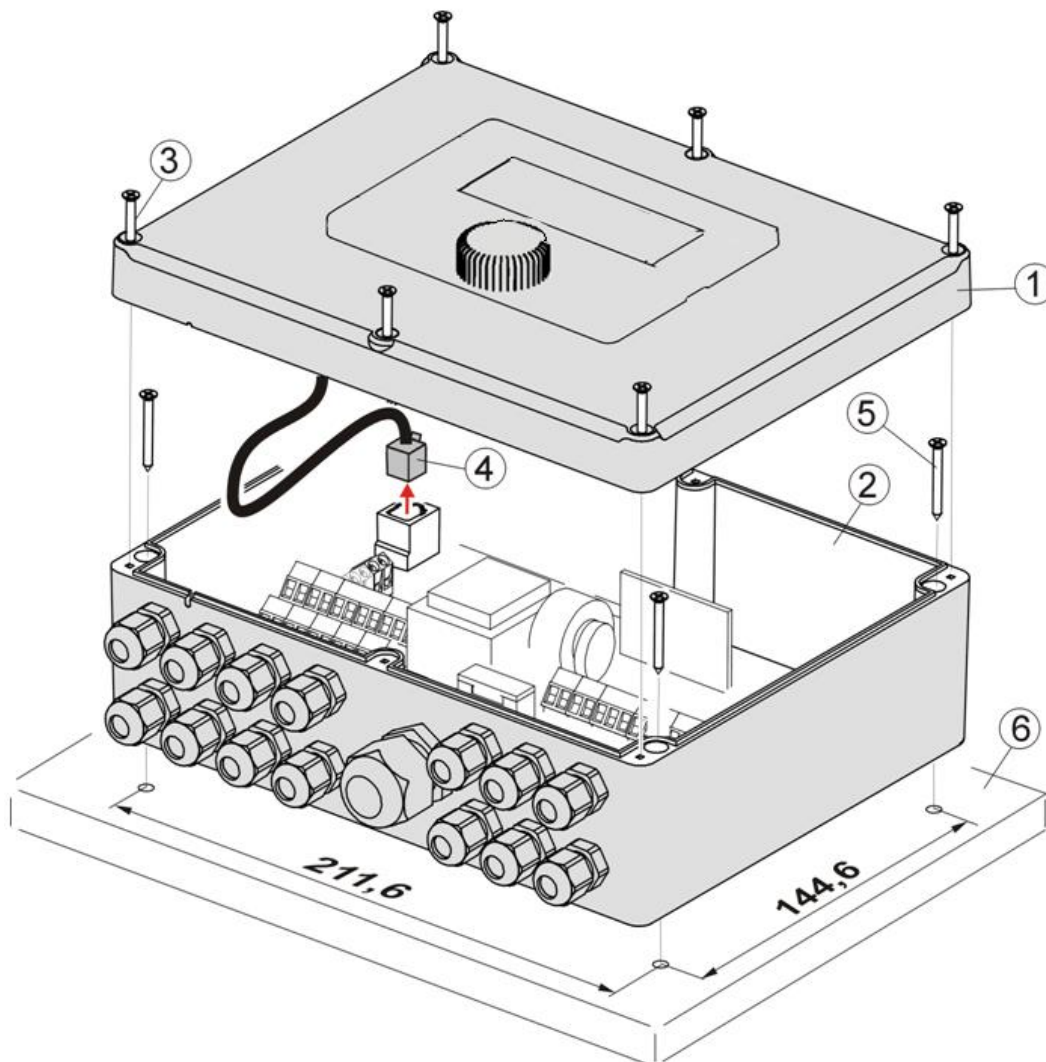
Befestigung des Steuergerätes an die Montagefläche: 1- Deckel, 2- Gehäuse, 3- Schraube für Deckel, 4- Stecker, 5- Schraube für die Befestigung an der Montagefläche, 6- Montagefläche.
